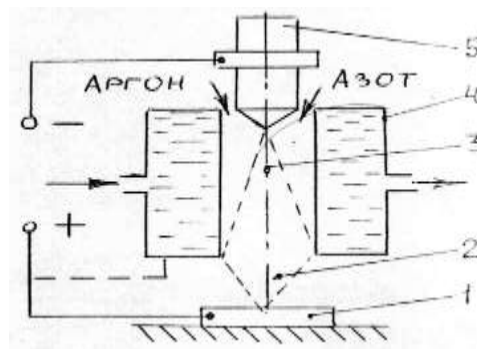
Схема плазменной головки: 1 – заготовка; 2 – плазменная струя; 3 – дуговой разряд; 4 – медный водоохлаждаемый электрод; 5 – вольфрамовый электрод
